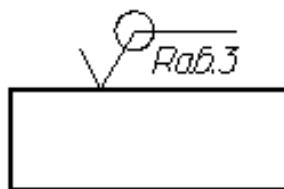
Обозначение одинаковой шероховатости поверхностей образующих замкнутый контур
